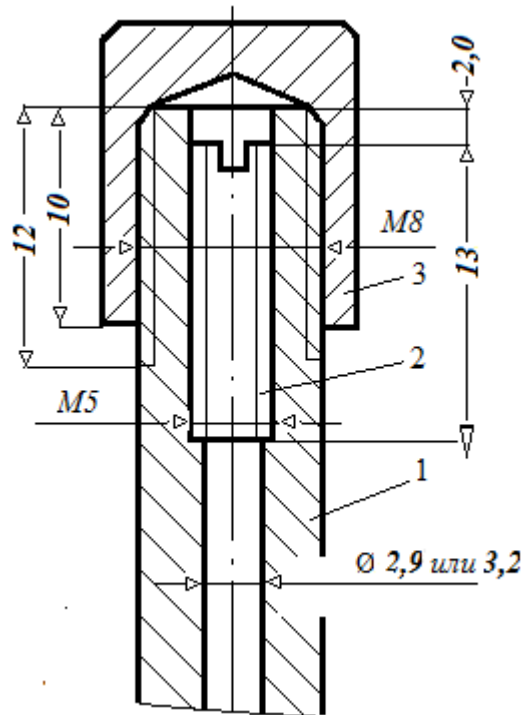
Схема предложенного запирающего устройства с приблизительными конструктивными размерами: 1 – корпус; 2 – винт; 3 – колпачок
